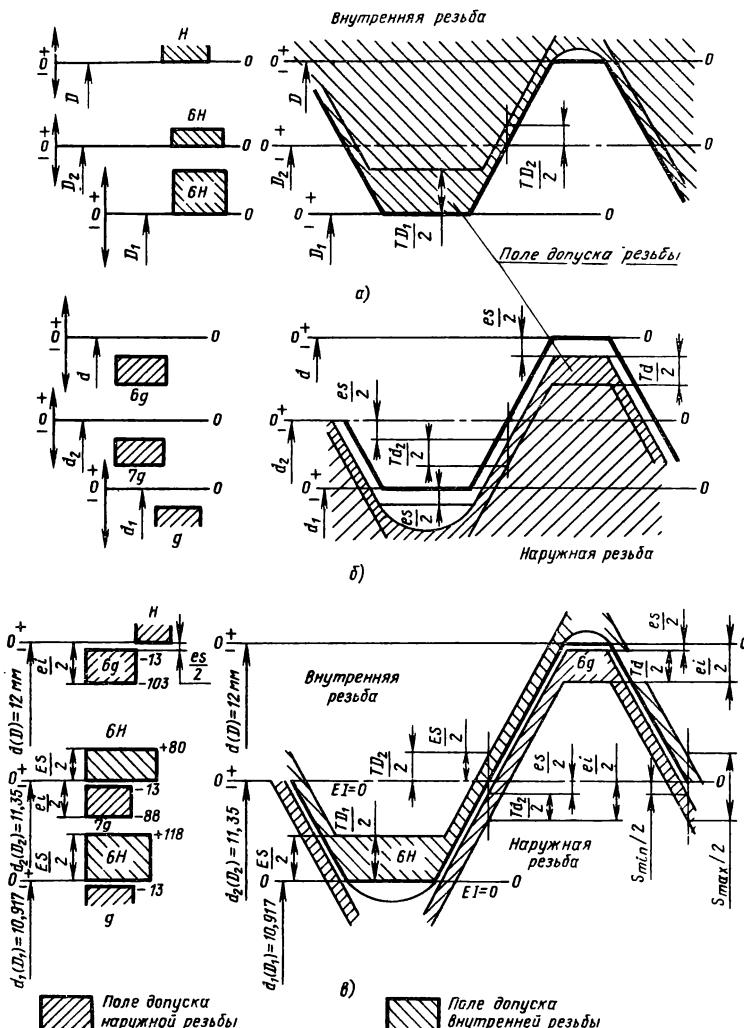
Схема расположения полей допусков внутренней (а), наружной (б) резьбы в соединении резьбовых деталей по посадке с зазором (в)
